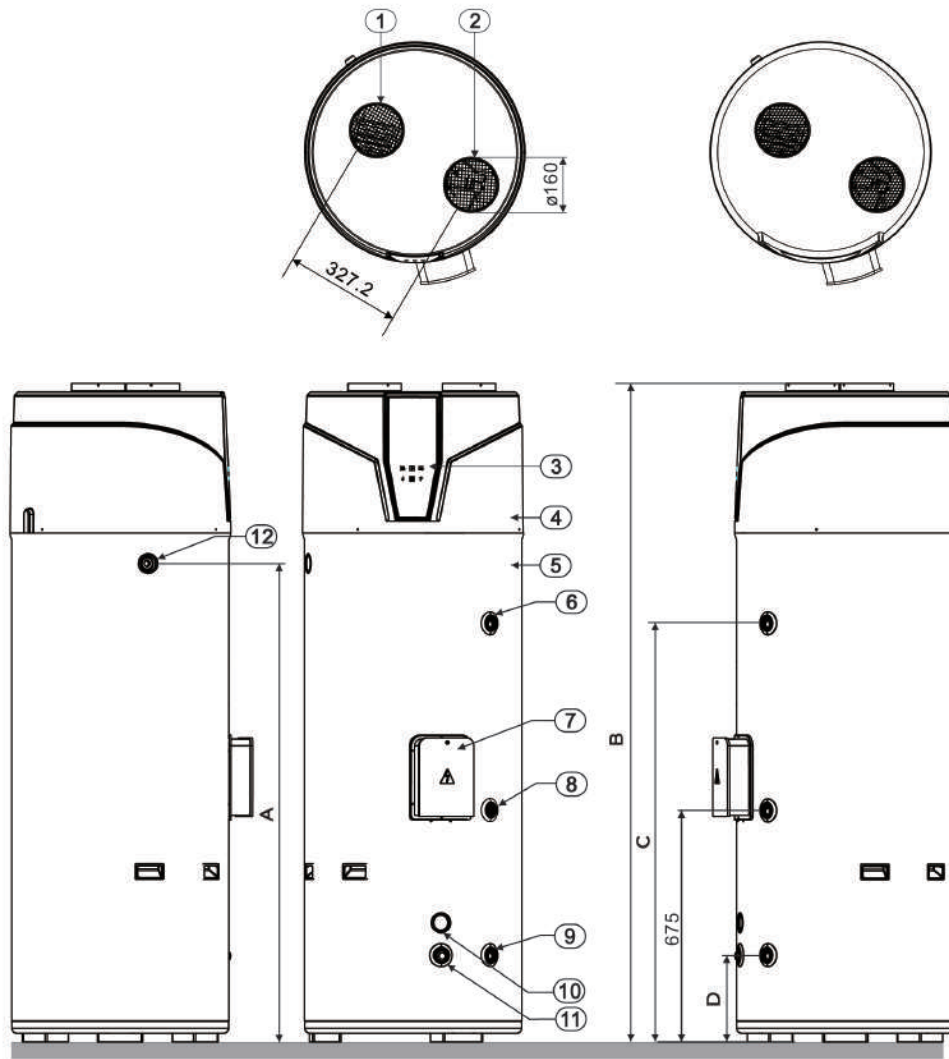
Vue et dimensions de l'appareil Stélios 2-250
